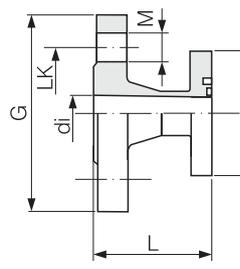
Dimensioni vista frontale del sensore DN 2...25
